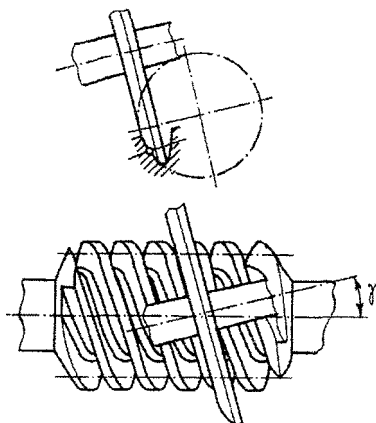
Схема обработки нелинейчатого червяка ZT с вогнутым профилем витка
